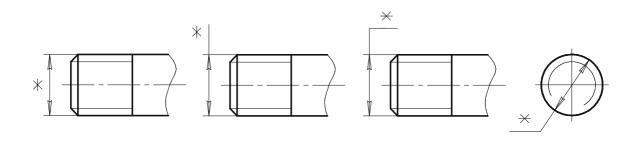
Варианты нанесения обозначений наружной резьбы
